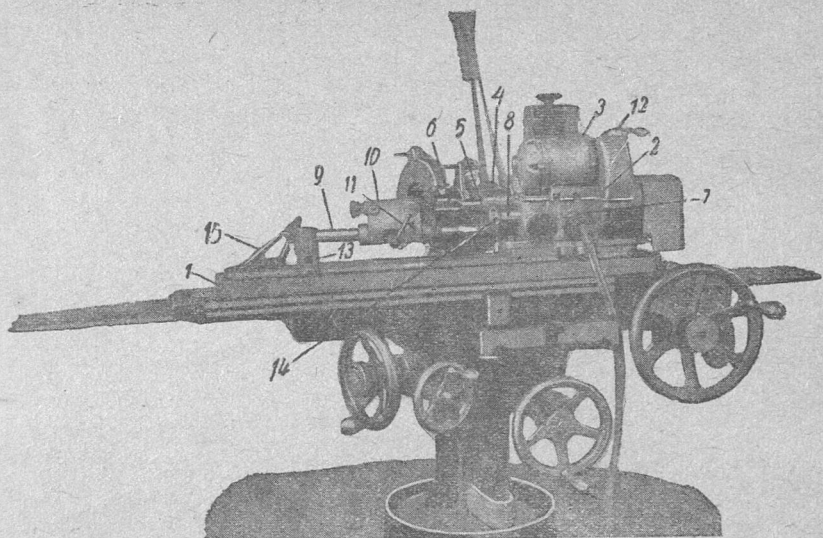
Прибор для шлифовки задней грани метчиков, установленный на заточном станке фирмы Герберт.
